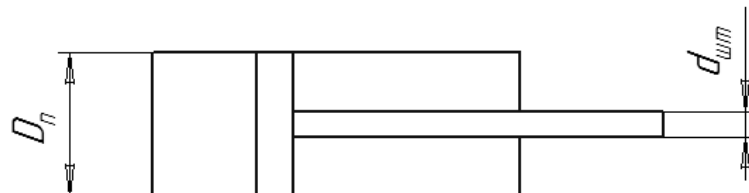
Схема пневмоциліндру двохсторонньої дії.
